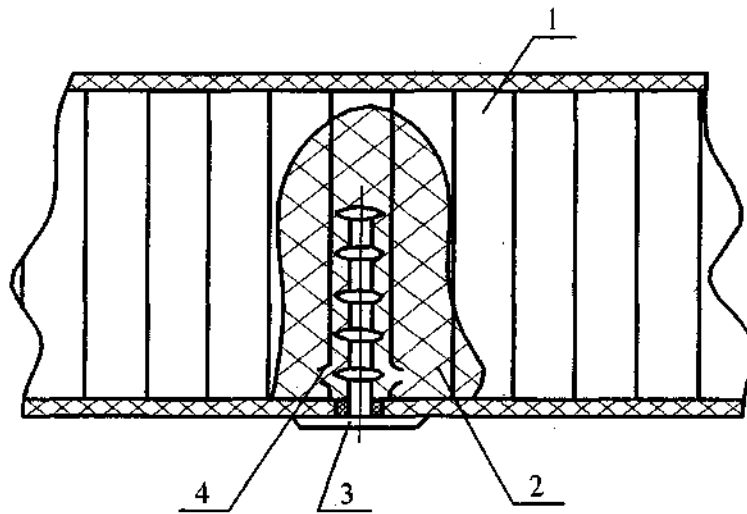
Ремонт отслоений с установкой заглушек типа "Винт"
